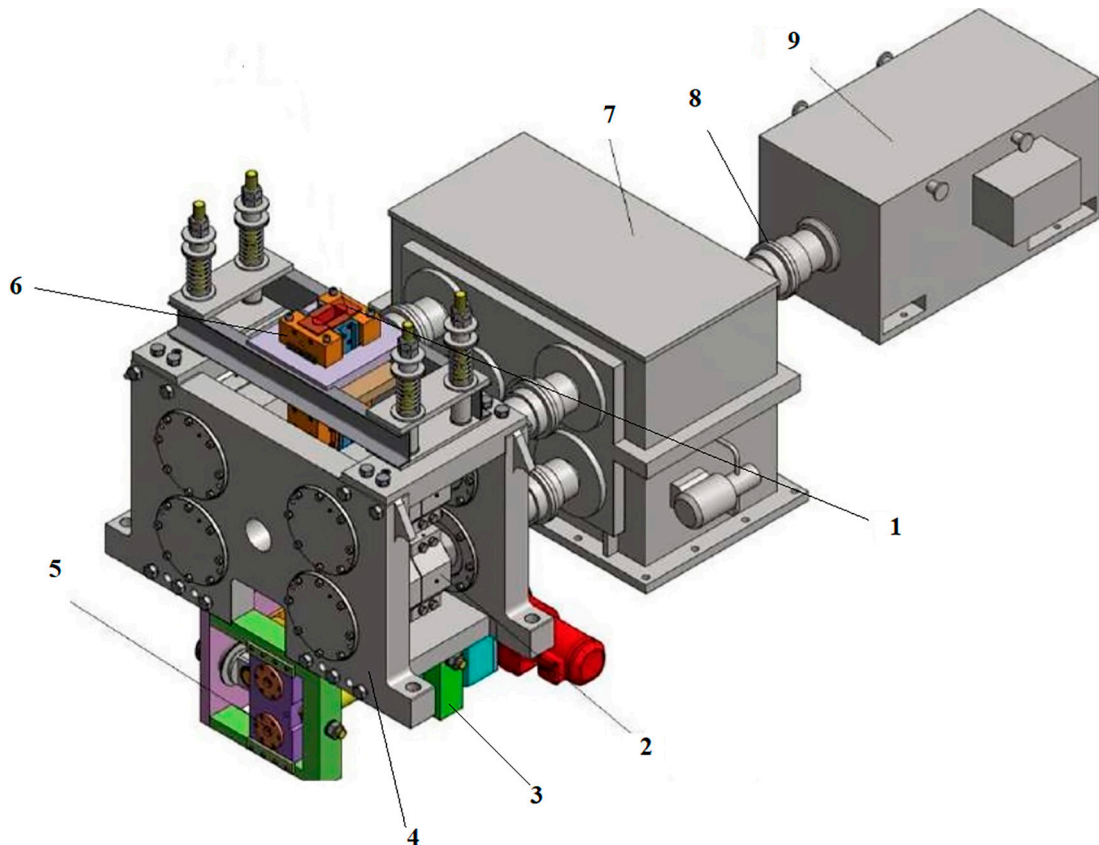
Конструктивная схема узлов установки: 1 – торец гильзы; 2 – крышка; 3 – корпус роликов; 4 – боковые поверхности; 5 – ролики; 6 – корпус кристаллизатора; 7 – комплект механической передачи; 8 – соединительные элементы основной передачи – муфты; 9 – узел привода
